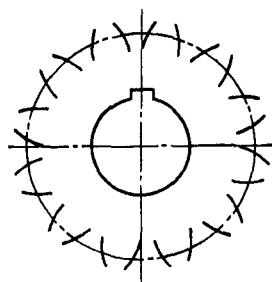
Исполнительные поверхности зубчатого колеса
